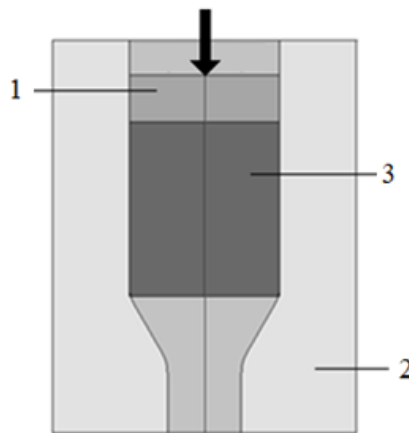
Розрахункова схема прямого видавлювання: 1 – пуансон; 2 – матриця; 3 – заготовка
